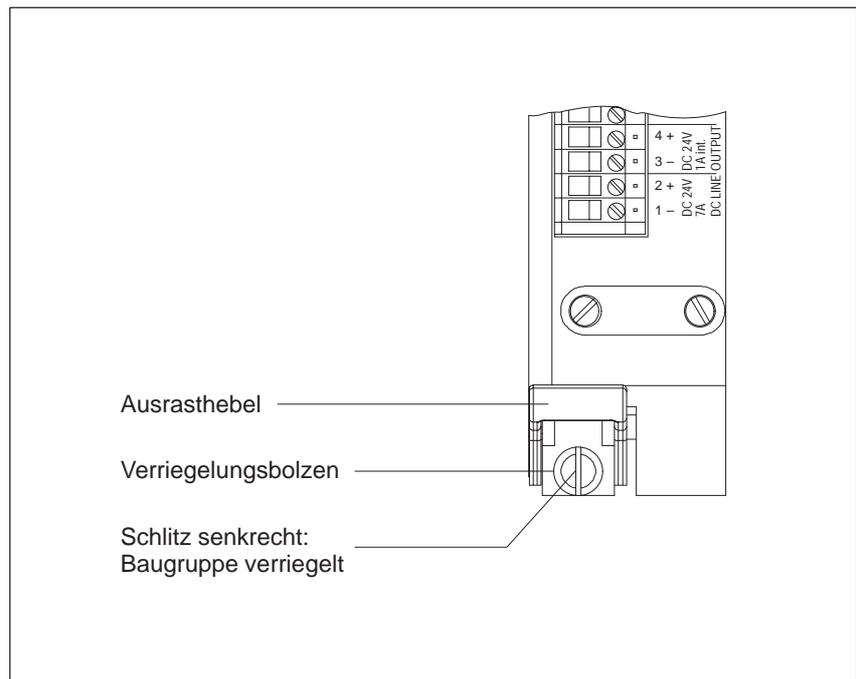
Frontansicht der Stromversorgungsbaugruppe, Verriegelungsmechanismus
